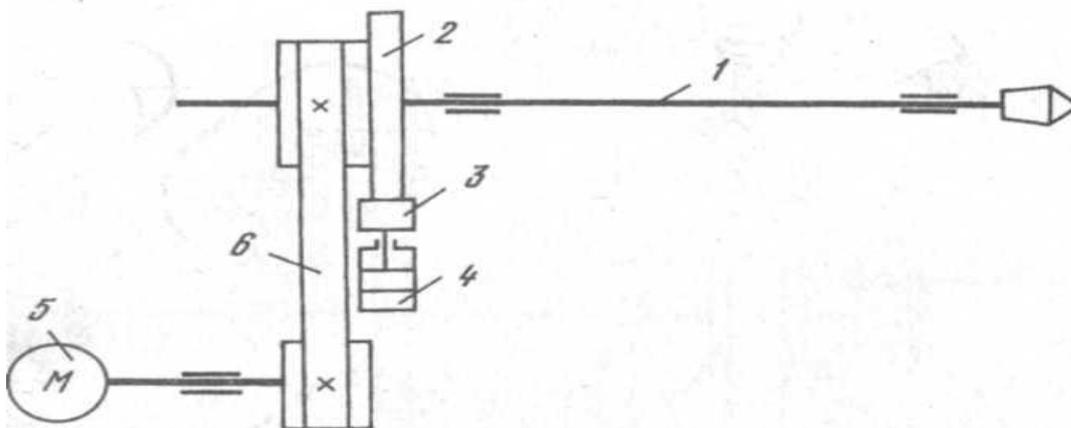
Принципиальная схема однодвигательного привода с фиксацией углового положения шпинделя..
